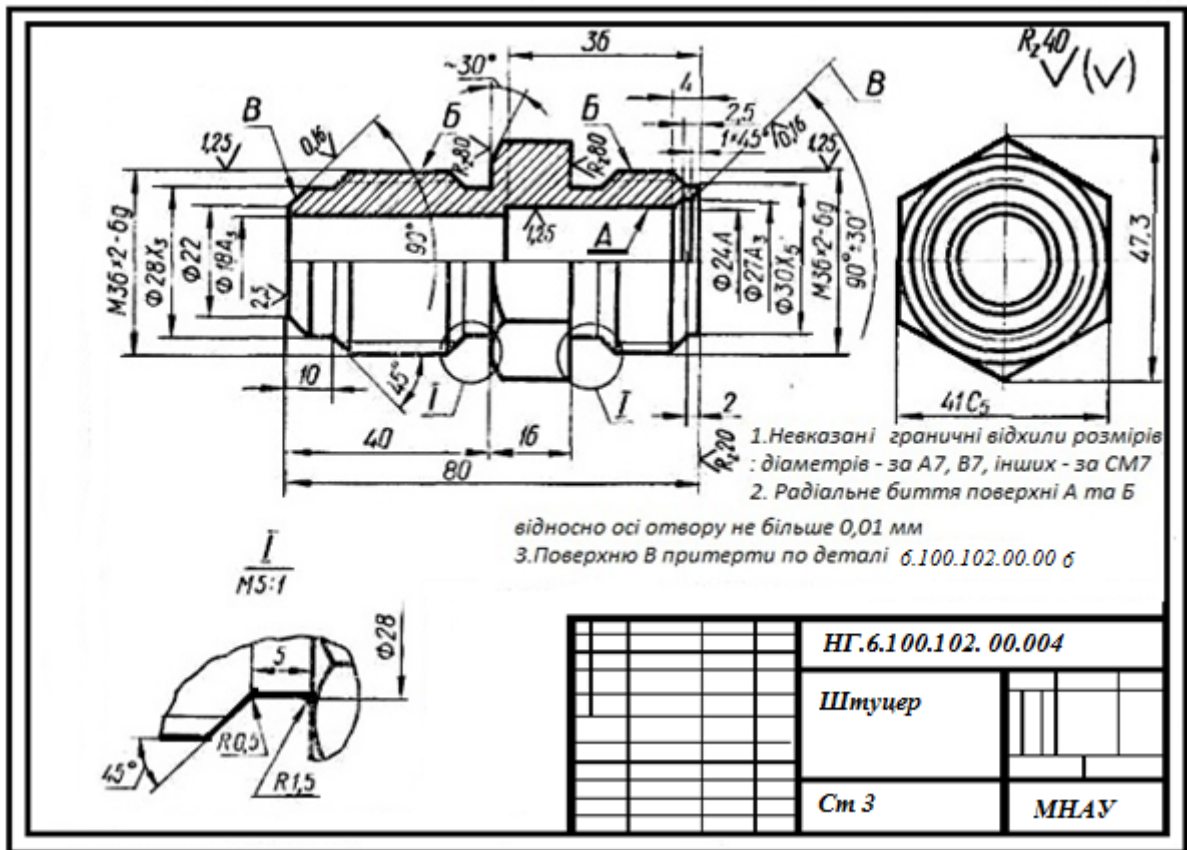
Робоче креслення деталі подвійного зворотного клапана
